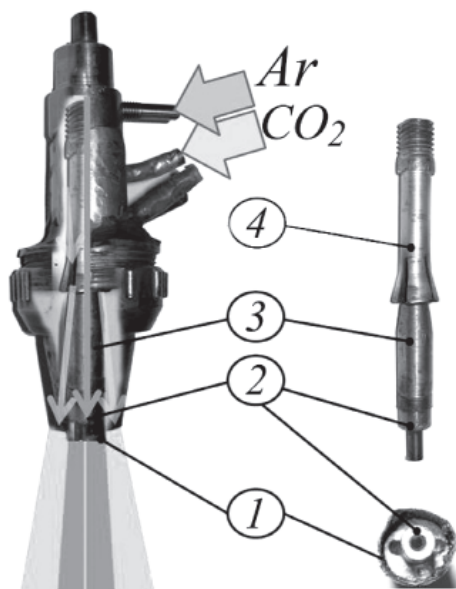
Горелка для комбинированной двухслойной защиты зоны сварки:
